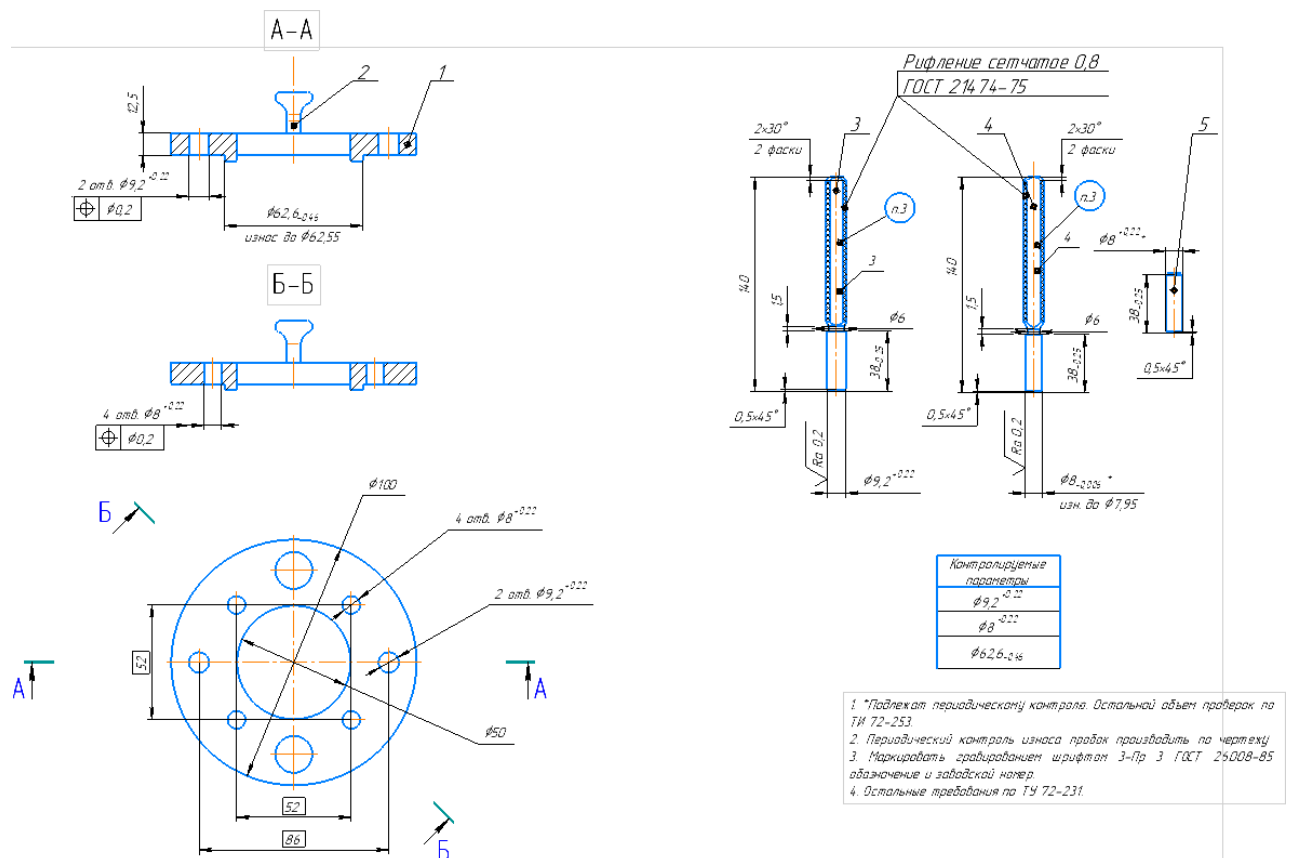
Приспособление для контроля допуска расположения
